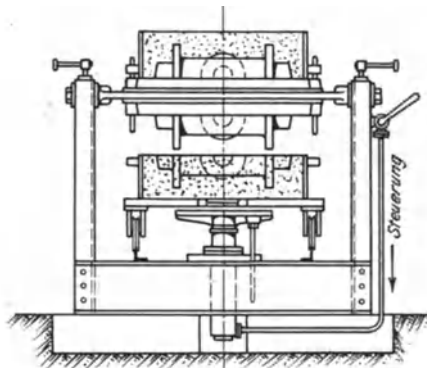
Handformmaschine mit hydraulischem Abheben und Wendeplatte 1885.
